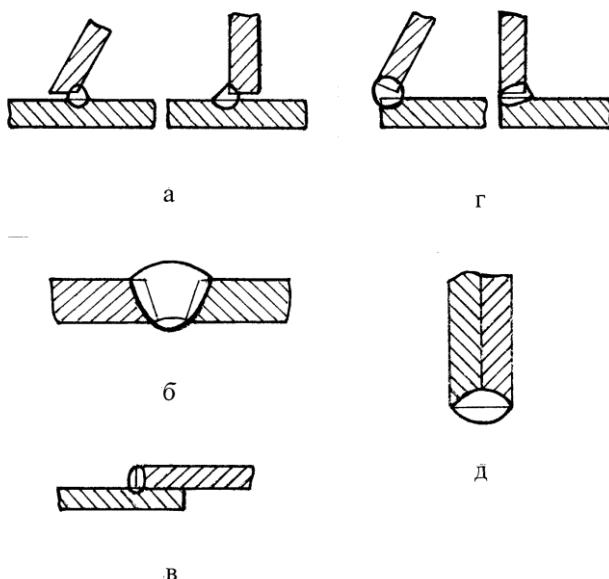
Виды сварных соединений: *а* – тавровое; *б* –стыковое; *в* – нахлесточное; *г* – угловое; *д* – торцовое
